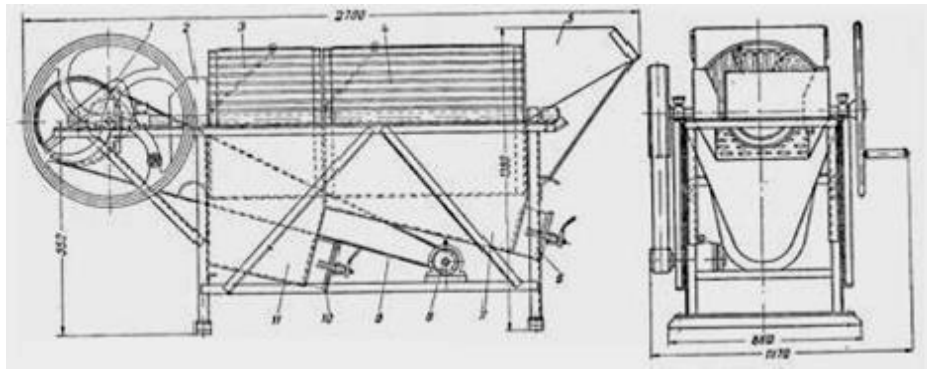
Схема барабанної двокамерної коренебульбоплодної мийної машини: 1 - кожух передавального механізму; 2 - випускний лоток; 3 і 4 - мийні барабани; 5 - загрузочний лоток; 6 і 10 - грязьові люки; 7 і 11 - корита для води; 8 - електродвигун; 9 - приводний ремінь
